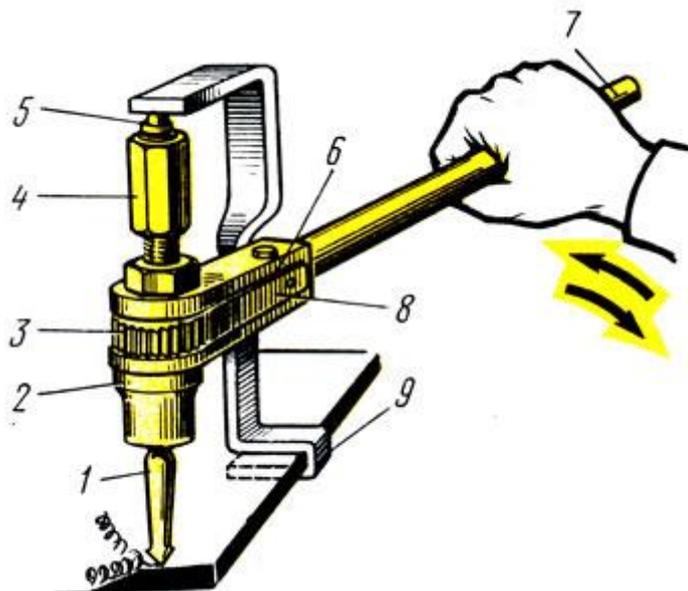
Трещотка: 1 - сверло, 2 - шпиндель, 3 - храповое колесо, 4 - гайка, 5 - центр, 6 - вилка, 7 - рукоятка, 8 - собачка, 9 - скоба
